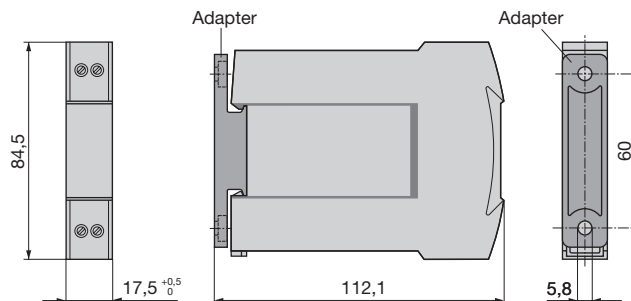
SINEAX TI 807-5.... (N17-Gehäuse) mit Adapter für direkte Wandmontage.
